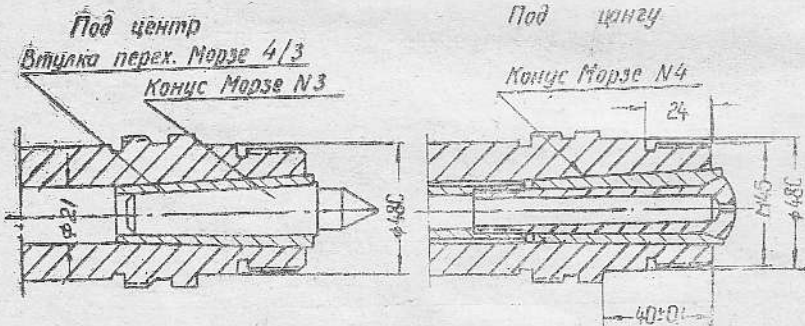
Габариты рабочего пространства. Посадочные и присоединительные базы станка
